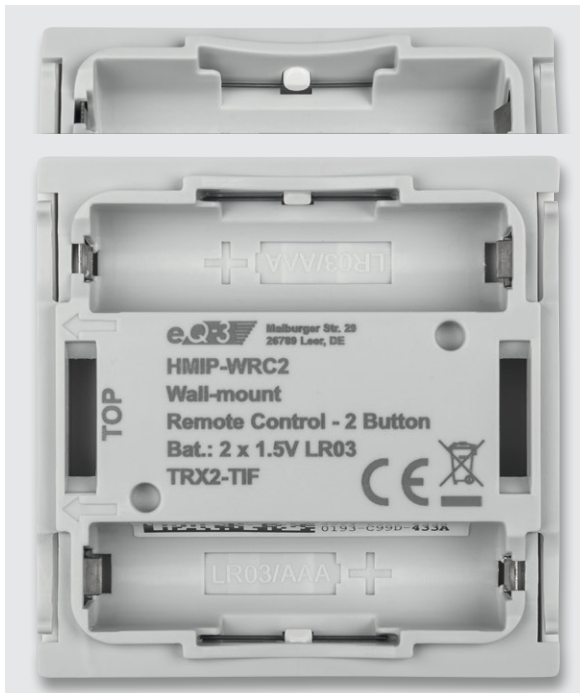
So wie oben zu sehen, wird der Federdraht auf jeder Seite unter den Kunststoffnasen des Gehäuses eingelegt. Unten ist das mit beiden Federdrähten bestückte, einsatzfertige Gerät zu sehen.
